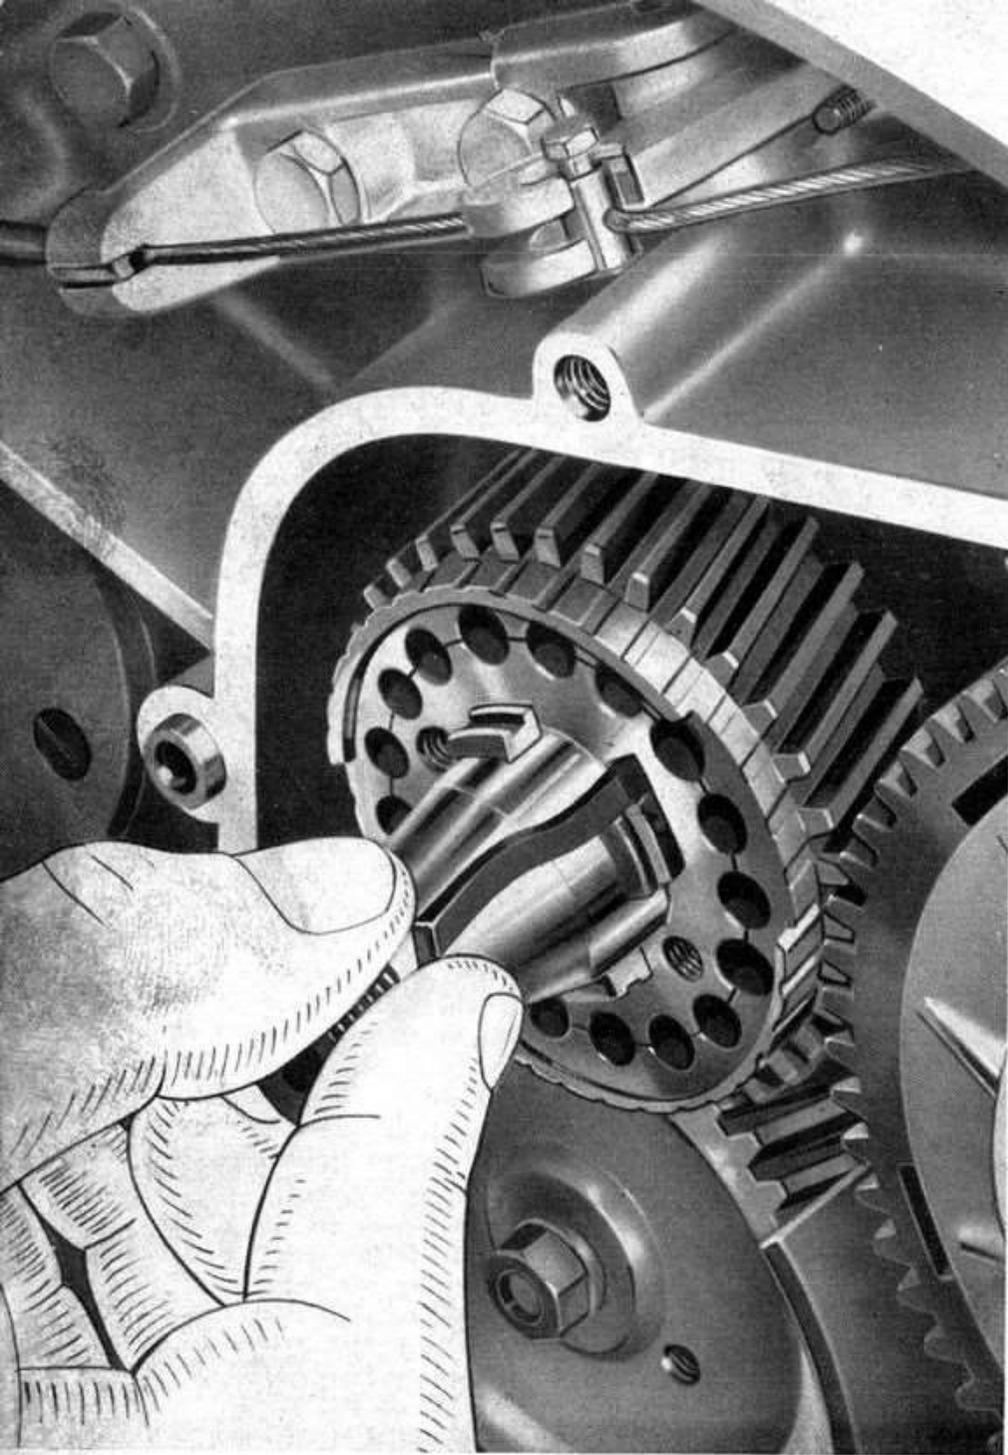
Come viene montata la molla a balestra per pignone elastico motore.
